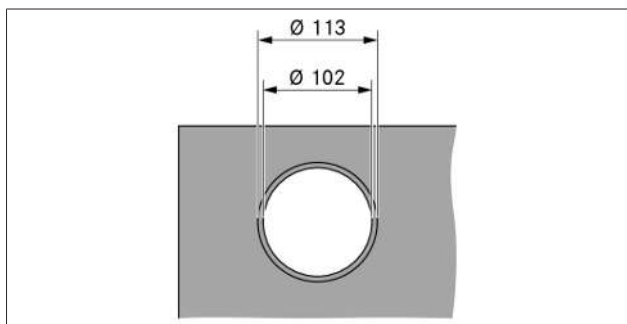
Rozmery výrezu pre montáž na povrch
